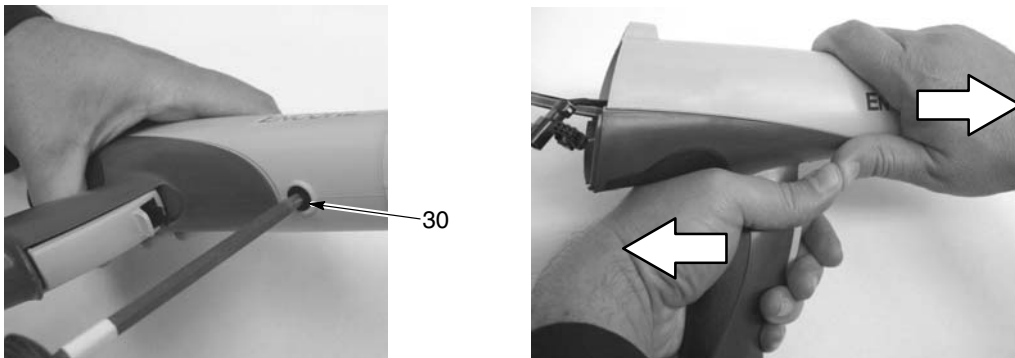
Снятие корпуса распылителя с рукоятки
